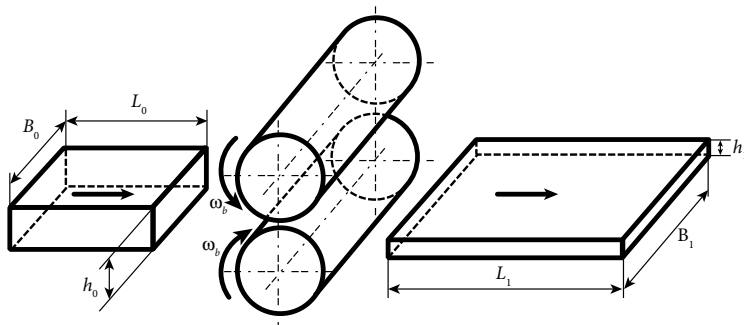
Схема формоизменения заготовки при плоской прокатке проката
